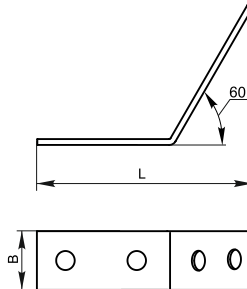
Уголок крепёжный наклонный 60° для STRUT-профиля
